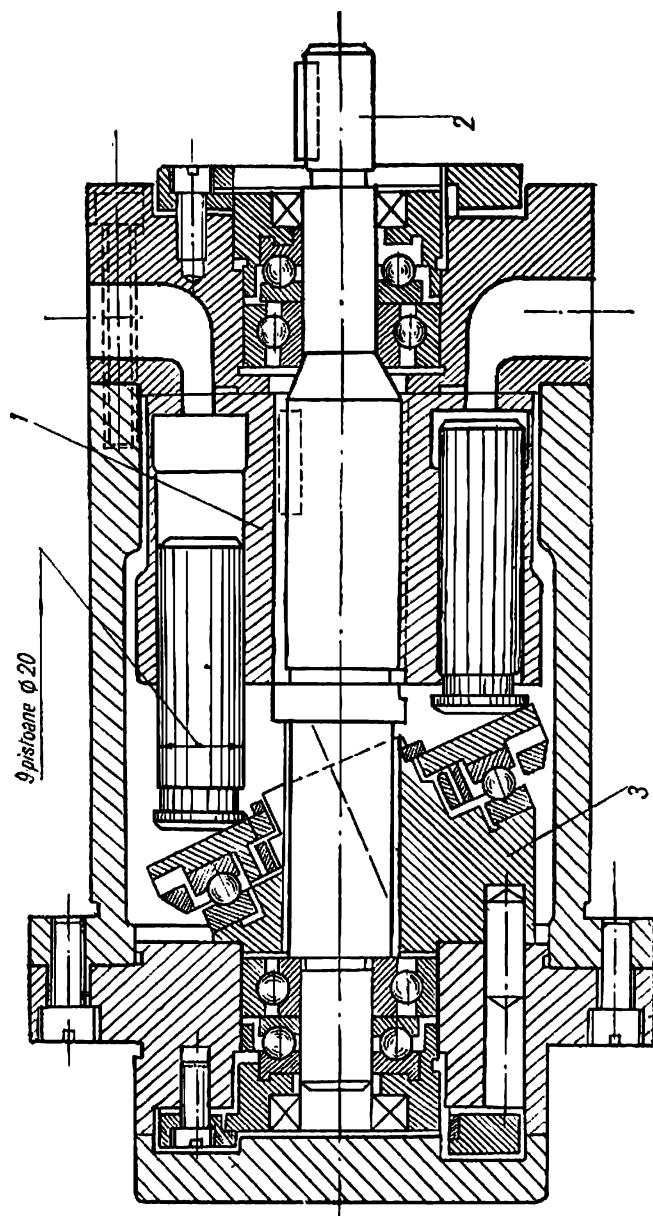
Motor hidraulic cu pistoane axiale și disc fix.
